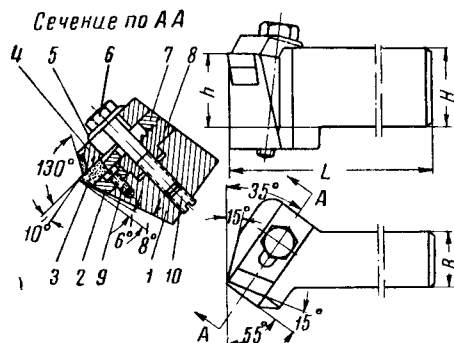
Резец с креплением пластинки твёрдого сплава усилиями резания
